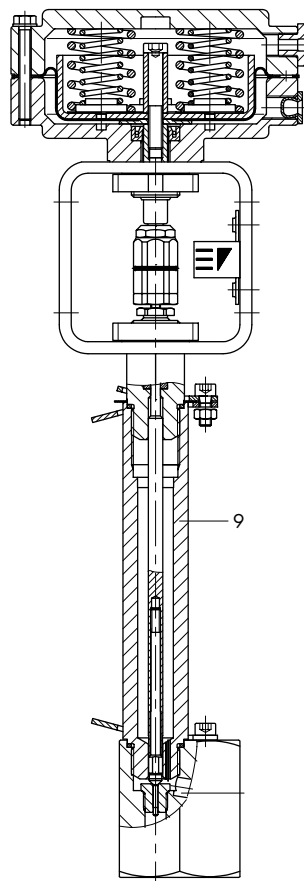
· Reguleringsventil Type 3510, Vinkelventil med isolerdel og aktuator Type 3271-52 (60 cm²)
